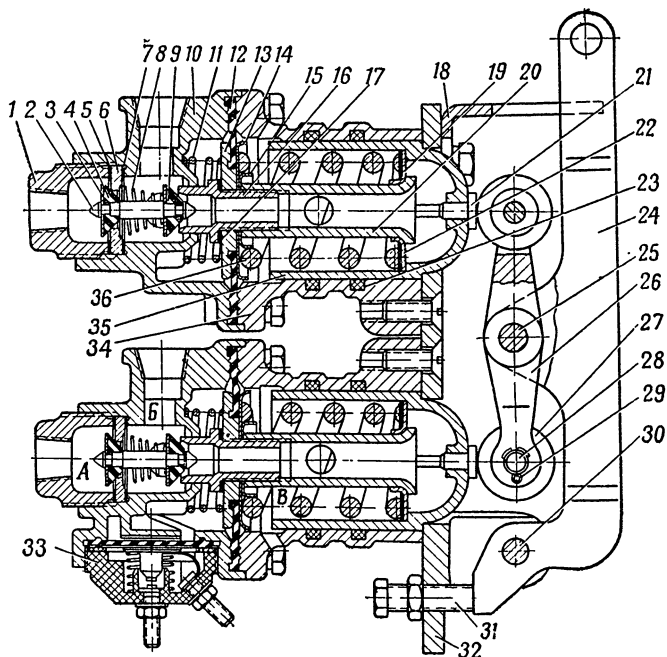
Конструктивная схема двойного тормозного крана с резиновыми клапанами и диафрагмами
